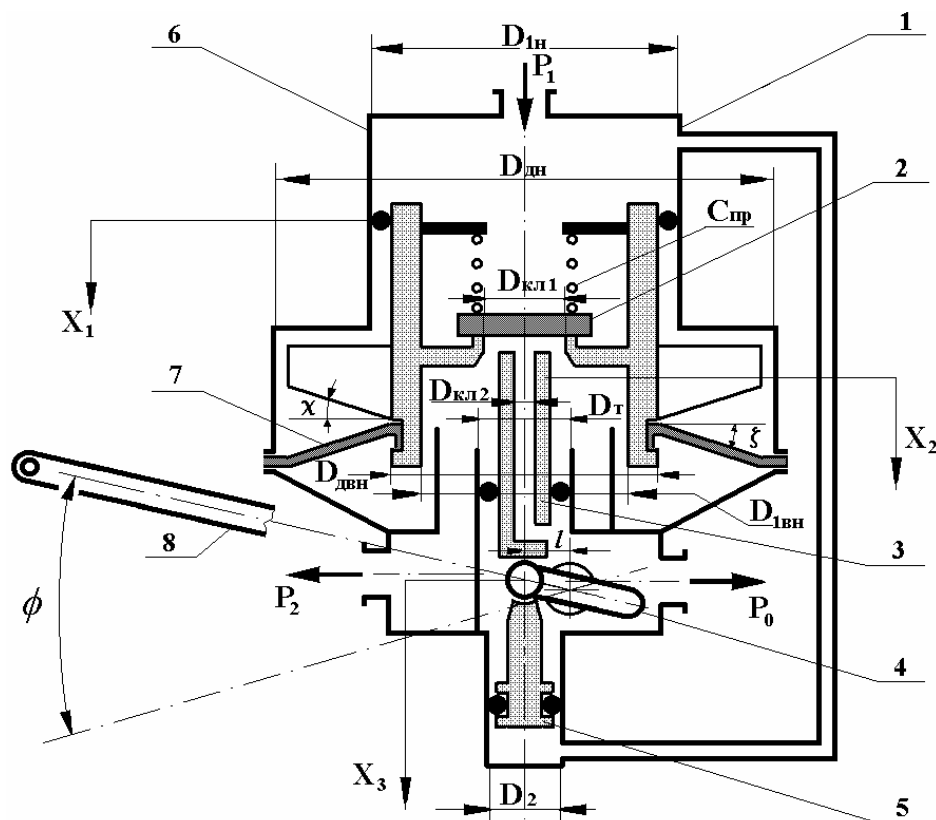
Схема автомобильного регулятора тормозных сил пневматического тормозного привода КамАЗ: корпус РТС; 2 – клапан следящей системы с пружиной; 3 – толкатель; 4 – ось с шаровой пятой; 5 – компенсирующий поршень; 6 – ступенчатый поршень; 7 – эластичная мембрана; 8 – рычаг, регулирующий давление в зависимости от загрузки автомобиля; ϕ – угол поворота рычага 8; X_1 – координата перемещения ступенчатого поршня; X_2 – координата перемещения толкателя 3
